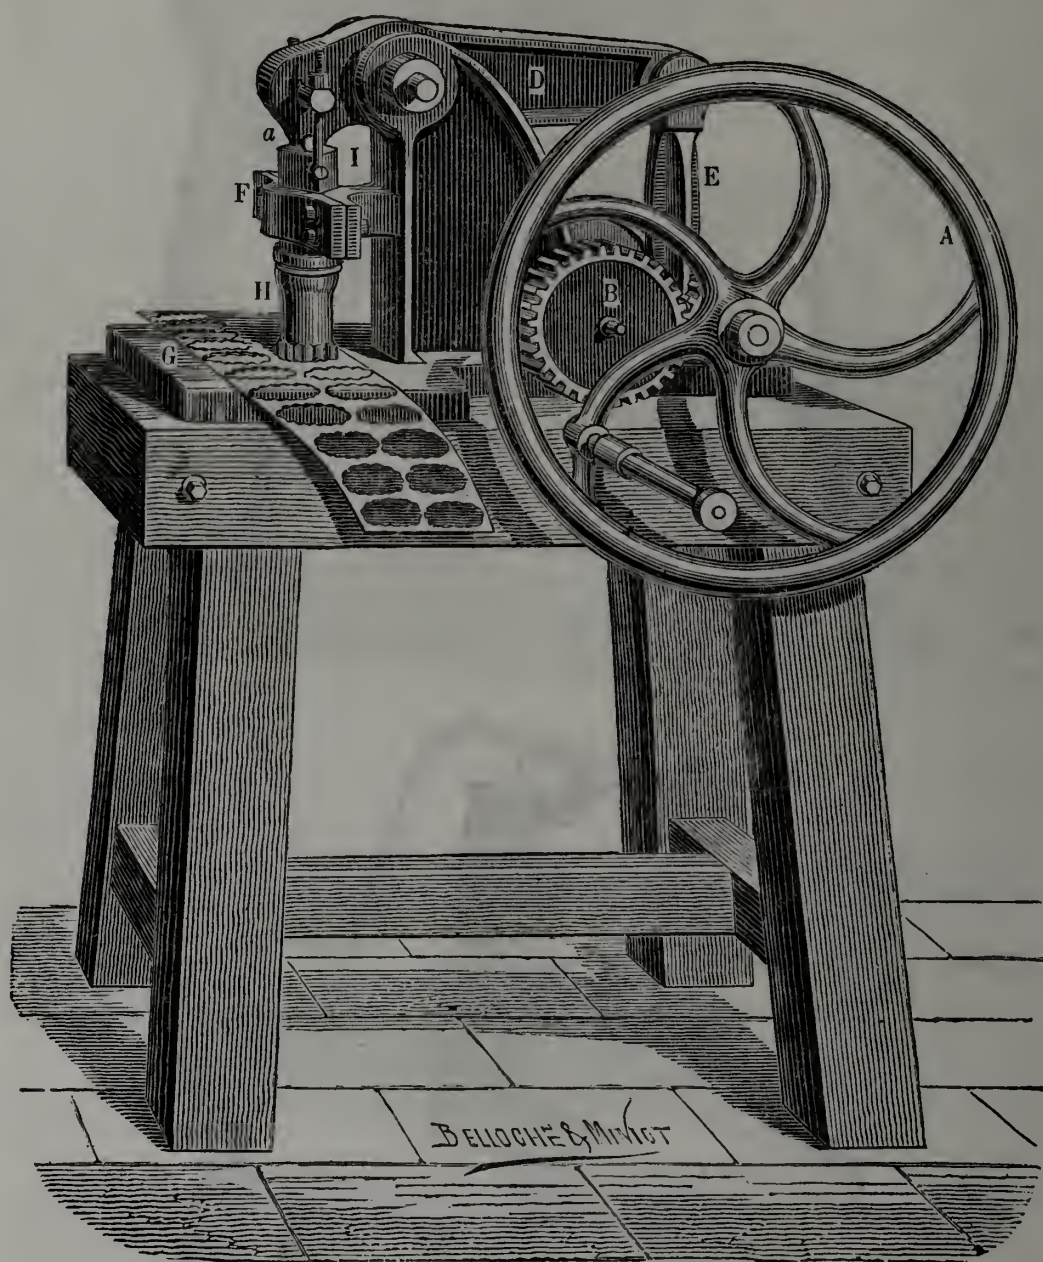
Machine à découper les fleurs artificielles, de M. Clément.
